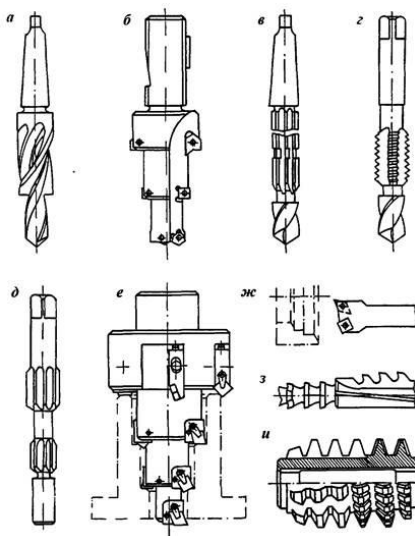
Комбинированные инструменты: а, б – сверло-зенкер, в – сверло резвертка, г – сверло-метчик, д – сдвоенная развертка, е – расточная головка или комбинированный зенкер, ж – комбинированный резец, з – круглошпоночная протяжка, и – червячная фреза-шевер
